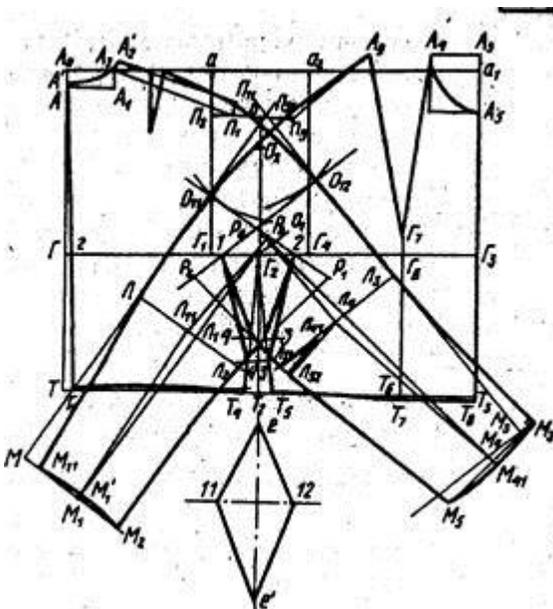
Чертеж конструкции передней и задней частей цельнокроеного рукава с ромбовидной ластовицей.
